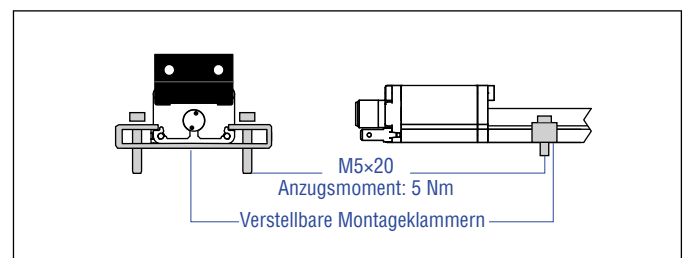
EL mit Montageklammern mit Zylinderschraube M5×20 (Artikelnr. 403 508)
